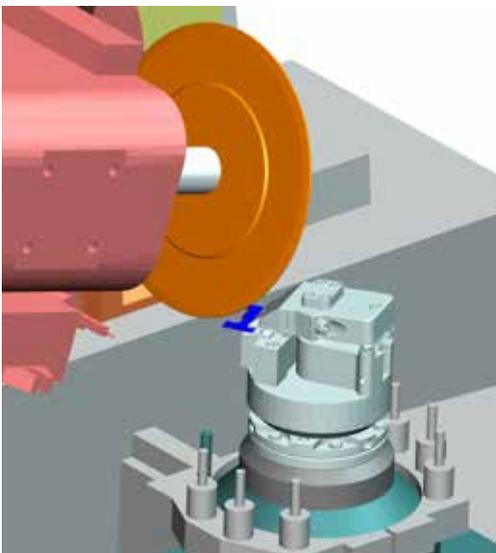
Unterscheidung rotatives Werkzeug oder Profilplatte
